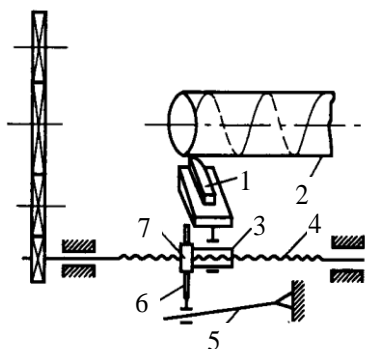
Коригуючий пристрій для нарізання точної різі:
